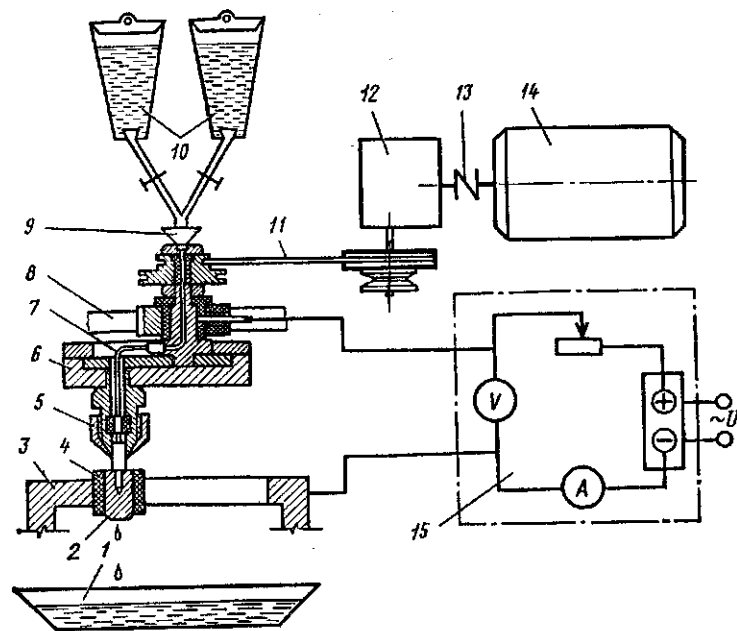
Схема установки для восстановления деталей электронатиранием гнезд подшипников в картере коробки передач:
